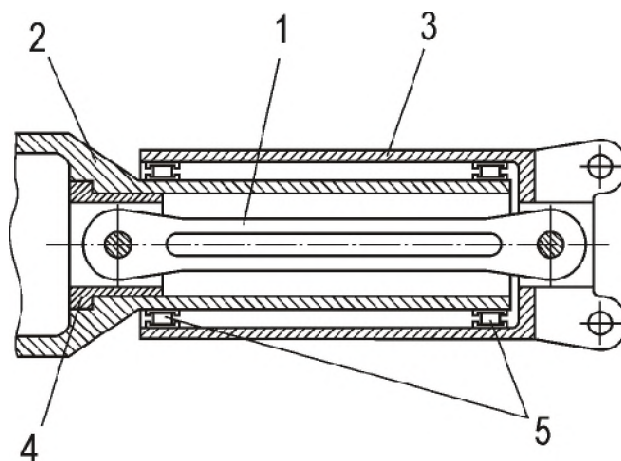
Схема осевого шарнира с торсионом: 1 – торсион; 2 – цапфа осевого шарнира; 3 – корпус осевого шарнира; 4 – вкладыш; 5 – радиальные подшипники.
